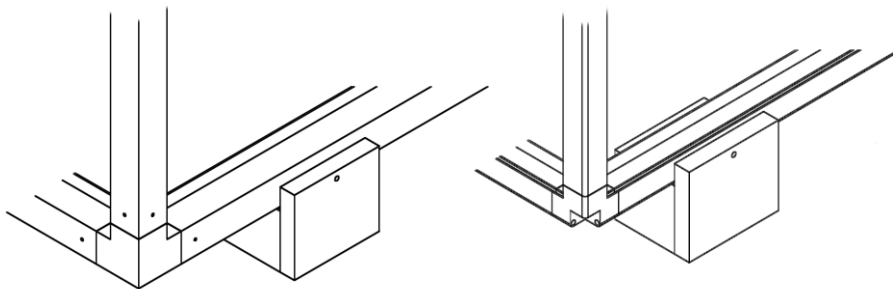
Транспортировочный башмак на корпусах Пролам и Аросио
